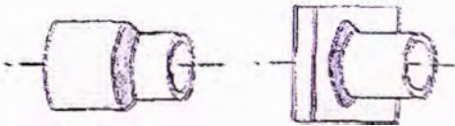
a: Posiciones para ensayo de tuberías o cañerías para soldadura de filete
